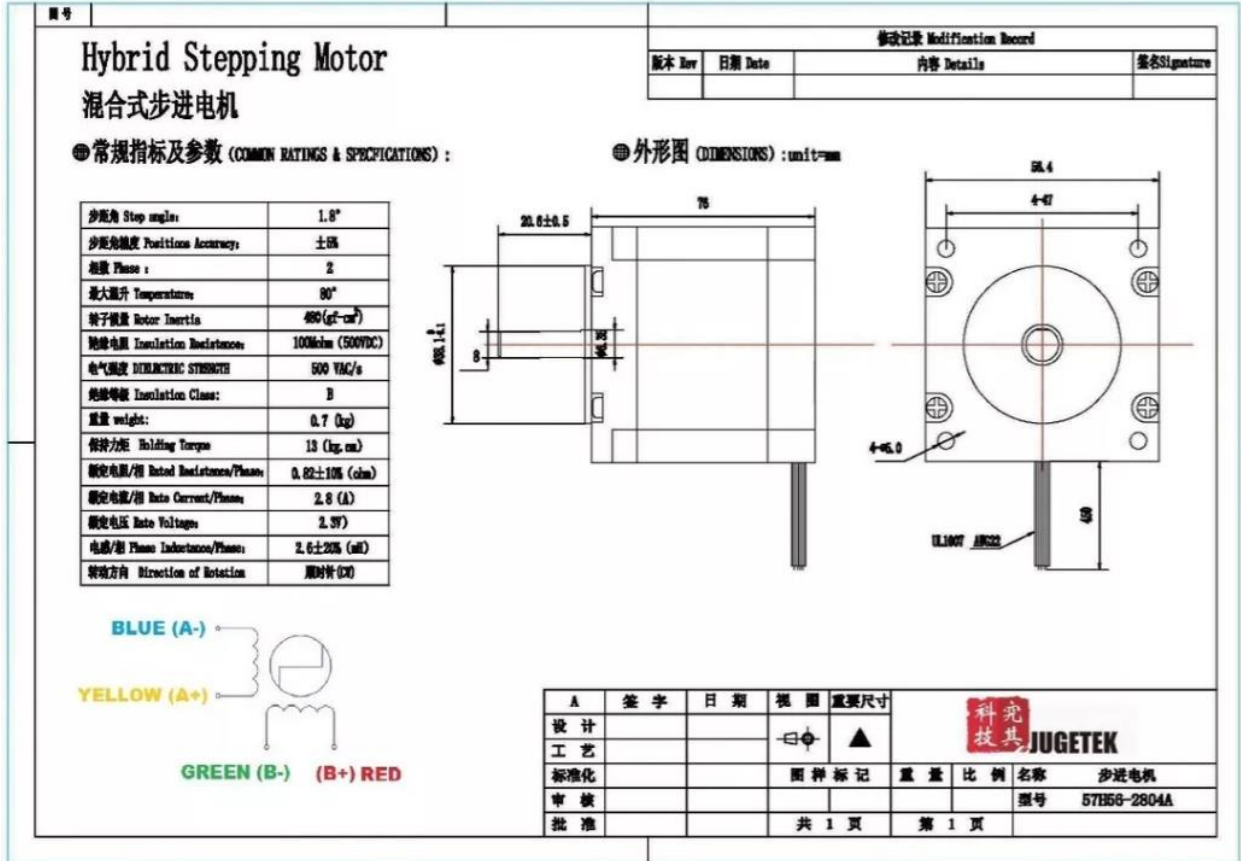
Ficha técnica del motor Nema 23 57H56-2804A [23]
